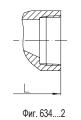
2 с резьбовыми муфтами - вертикальная установка
